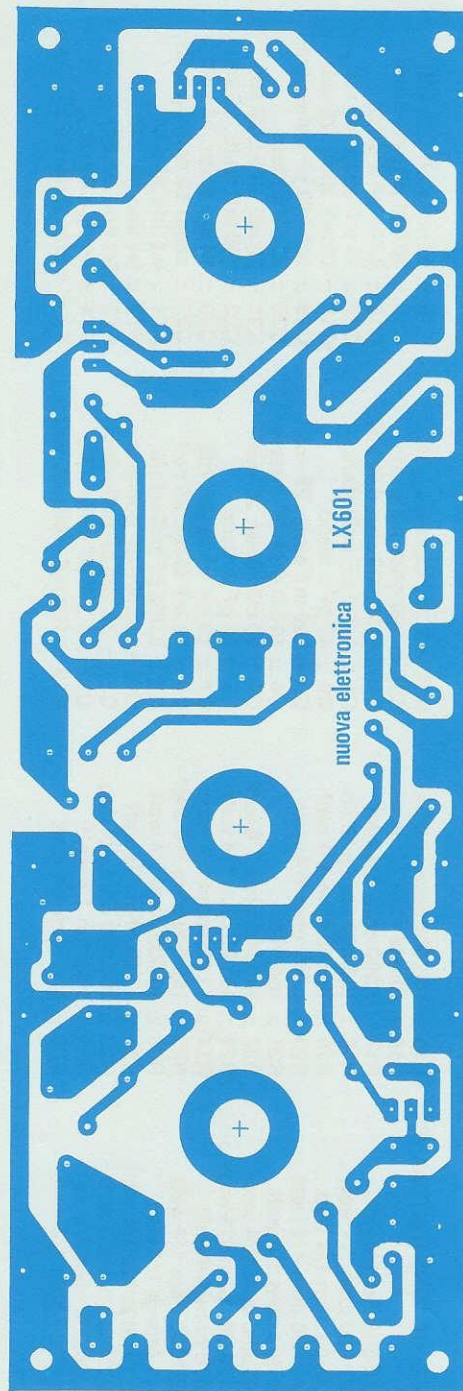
Il circuito stampato di questo preamplificatore è un doppia faccia, in questo disegno è visibile la parte inferiore.
